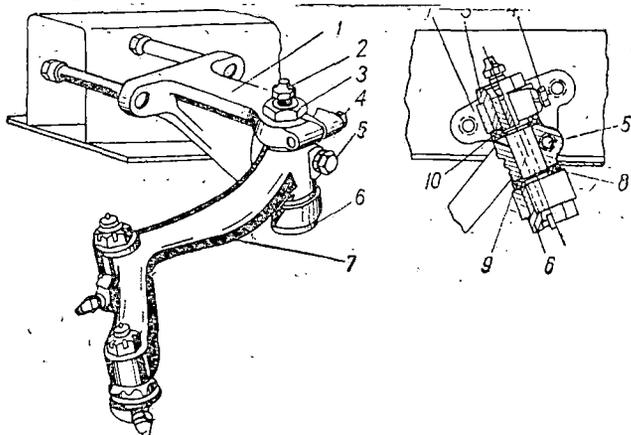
Установка маятникового рычага рулевого привода автомобиля ГАЗ-21 «Волга».
